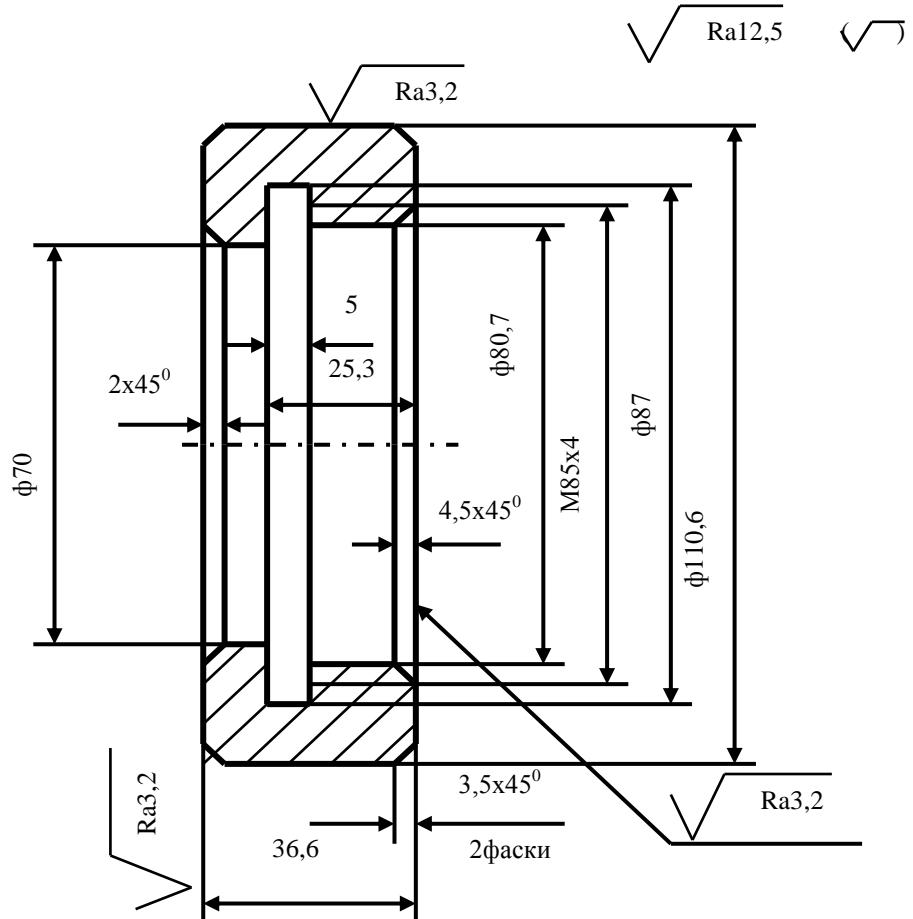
Чертеж токарной заготовки (оформляется на формате А4)
